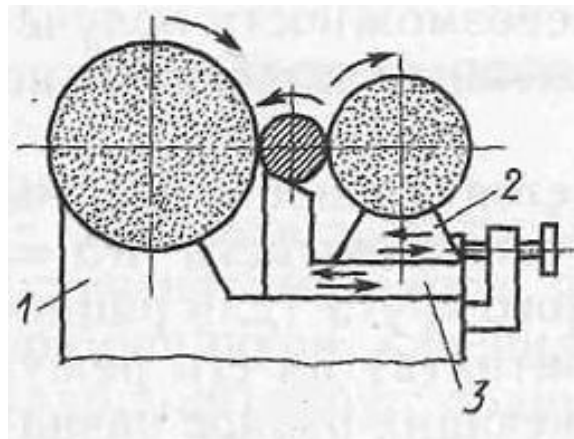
Принципиальная схема бесцентрового кругло-шлифовального станка:
